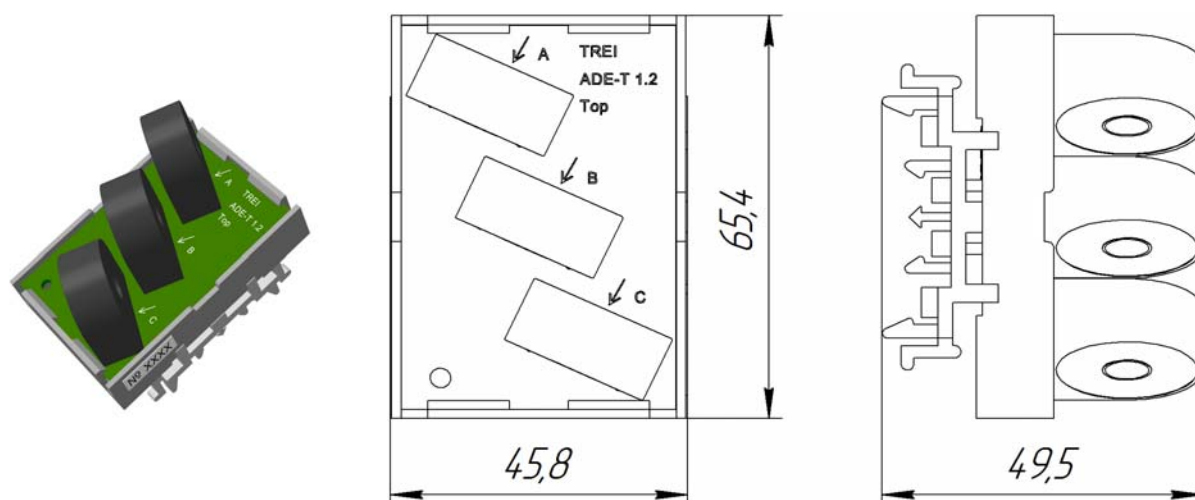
Общий вид и габаритные размеры блока M171N-T
